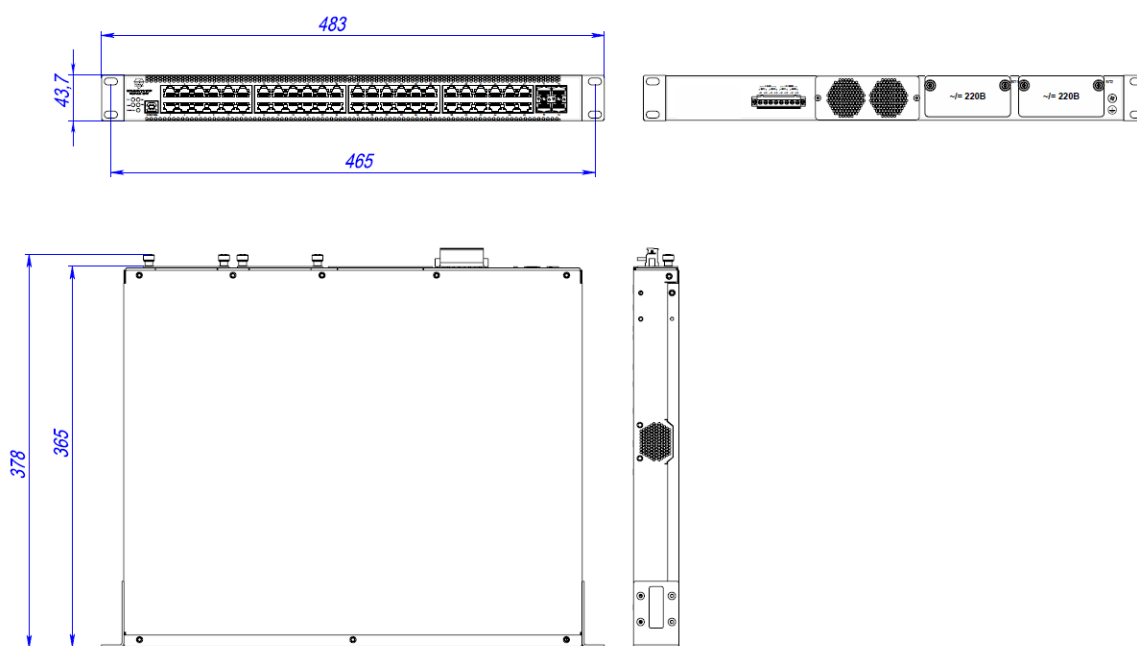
Внешний вид и габаритные размеры коммутатора
